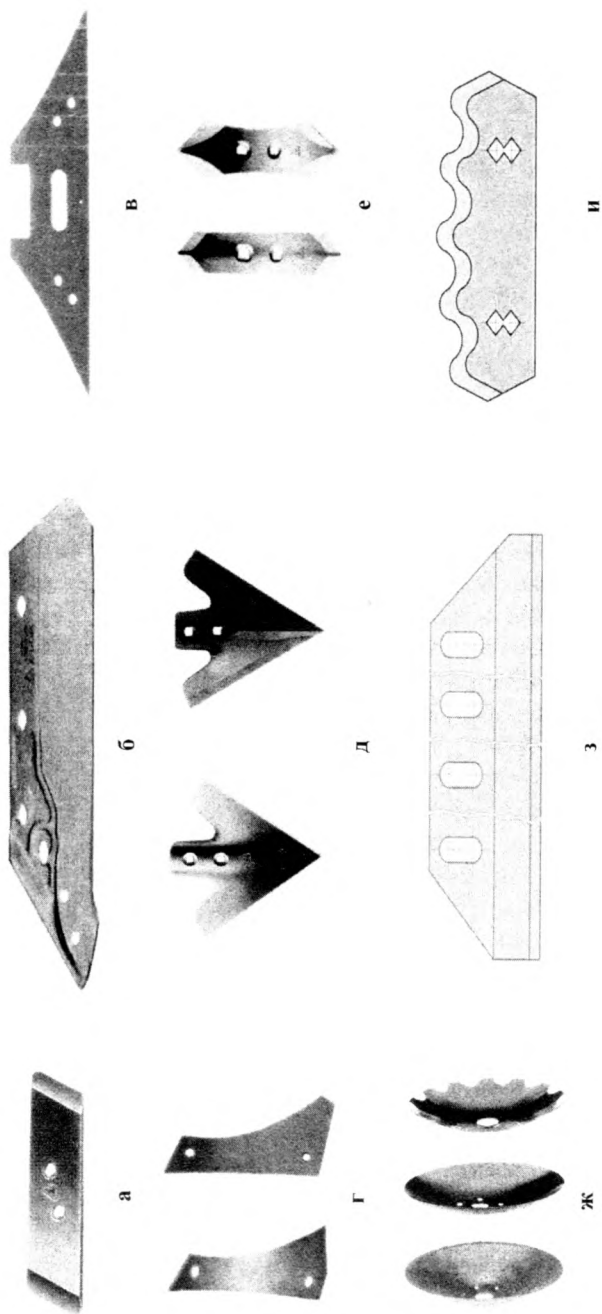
Типовые представители сменных деталей почвообрабатывающих и кормоуборочных машин:
